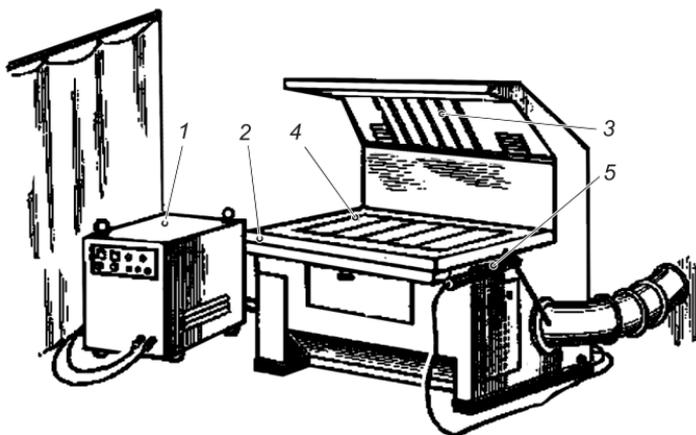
Общий вид стационарного поста для ручной дуговой сварки (ММА)
